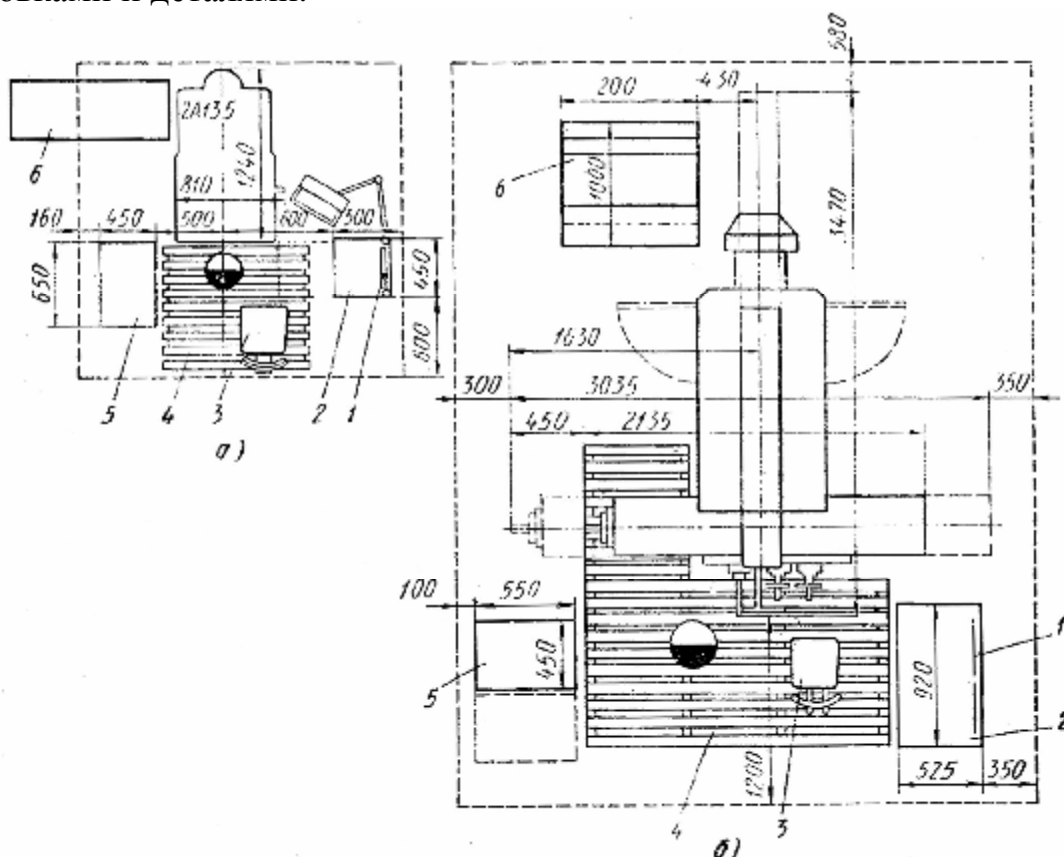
Планировка рабочих мест сверловщика (а) и фрезеровщика (б):
